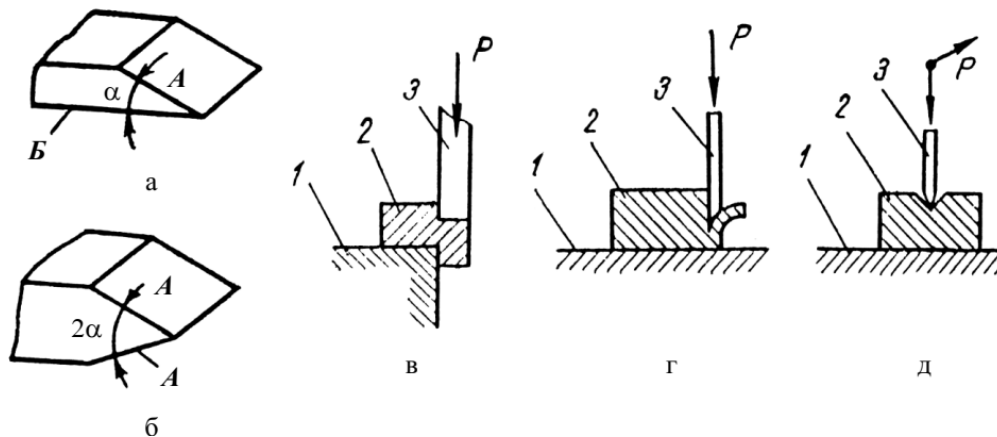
Схеми різання: а – ніж з однією різальною кромкою; б – ніж з двома різальними кромками; в – різання пуансоном; г – різання клином з однією кромкою; д – різання клином з двома кромками; 1 – опорна поверхня; 2 – оброблюваний матеріал; 3 – різальний елемент
